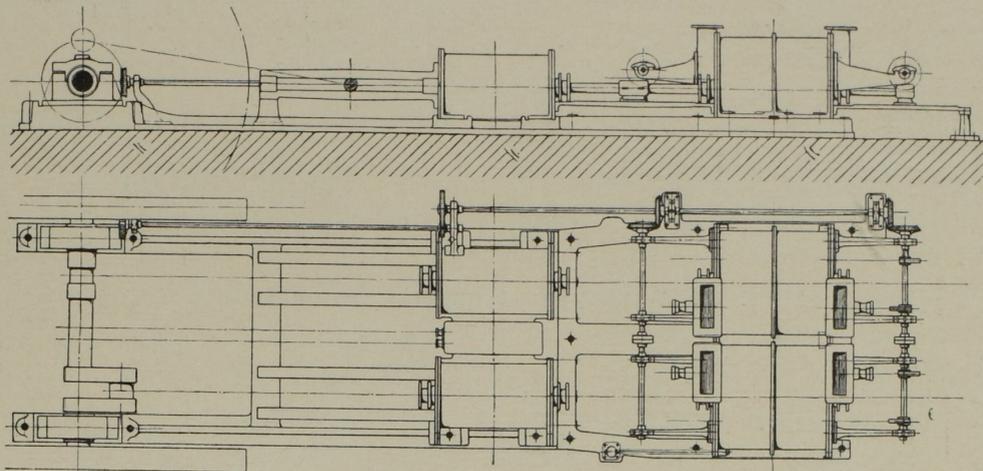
Seitenansicht und Grundriss. Massst. 1:100.
